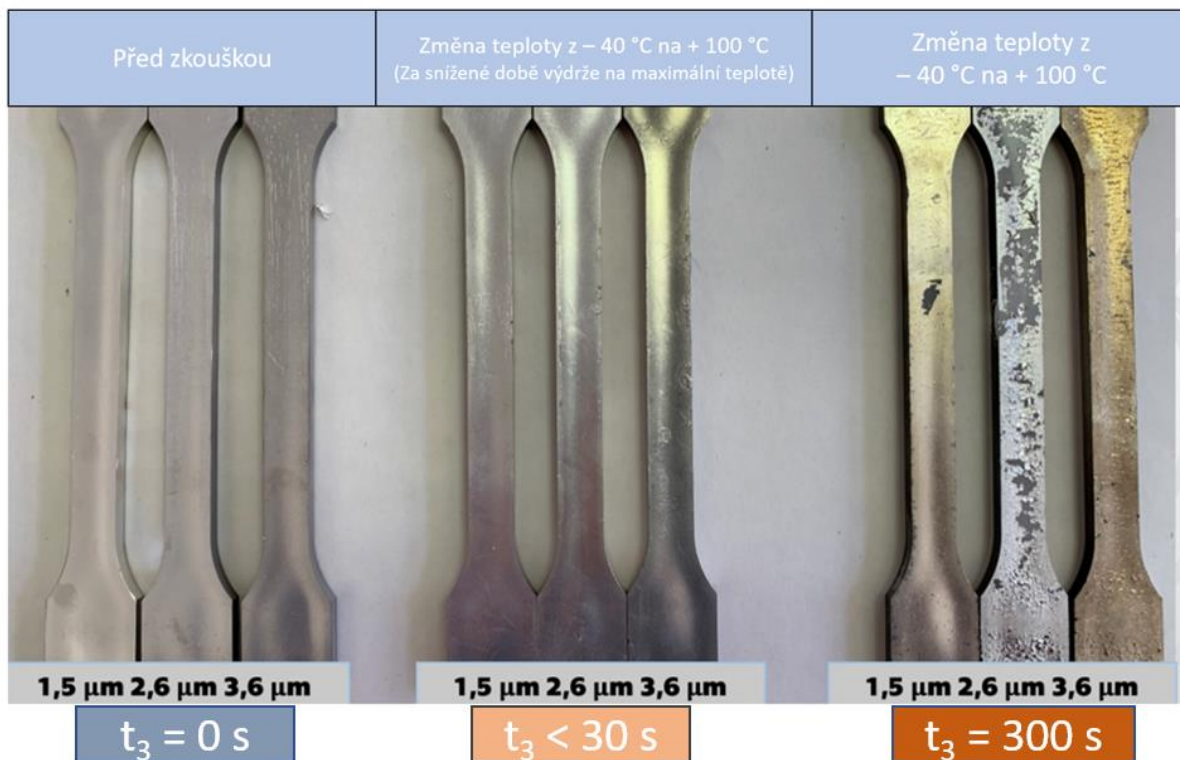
Snímek zachycující tloušťku měděného povlaku na materiálu C
